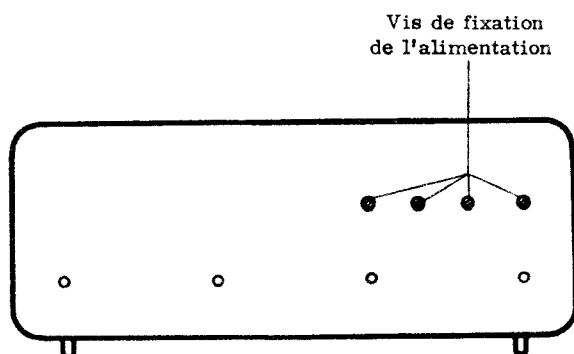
Vue arrière de l'émetteur-récepteur.
